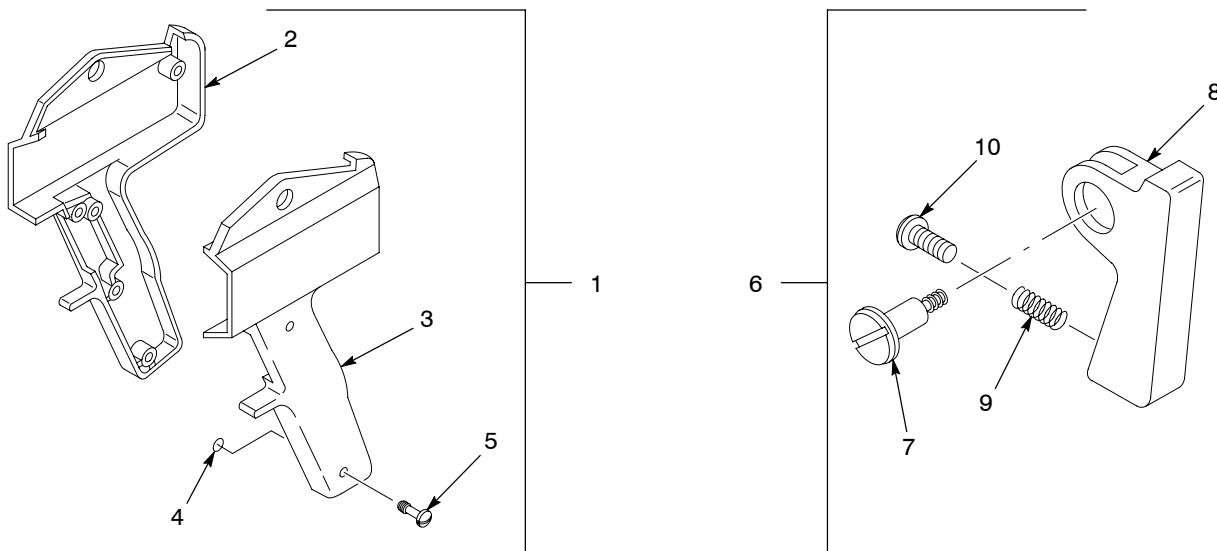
Ремонтные комплекты для рукоятки и спускового крючка
